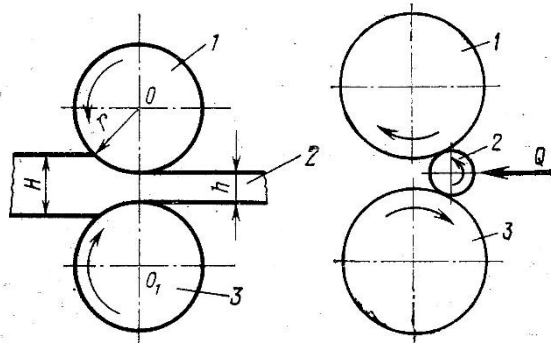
Схема продольной прокатки: 1-верхний валок; 2-прокатываемая полоса; 3-нижний валок
